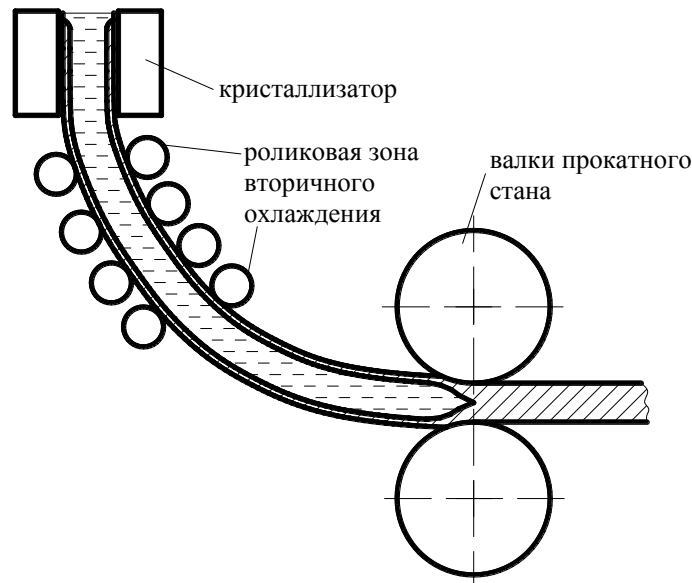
Схема ЛПА з «м'яким» обтисканням заготовки
